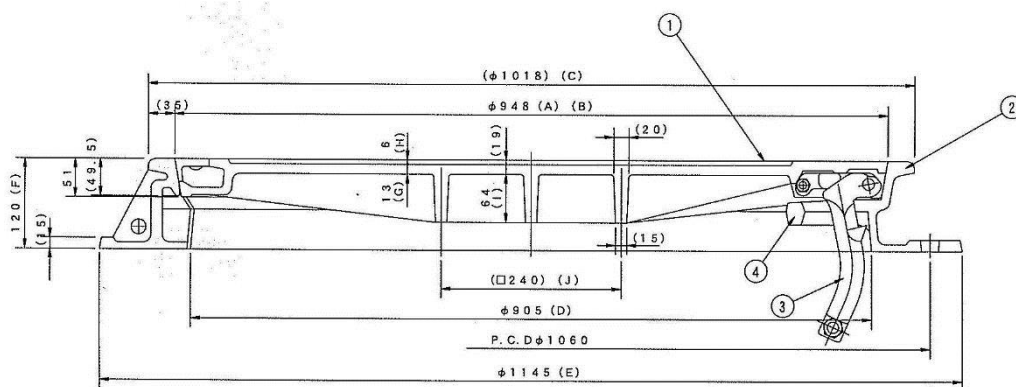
φ900鉄蓋 (T-25) 平面図
